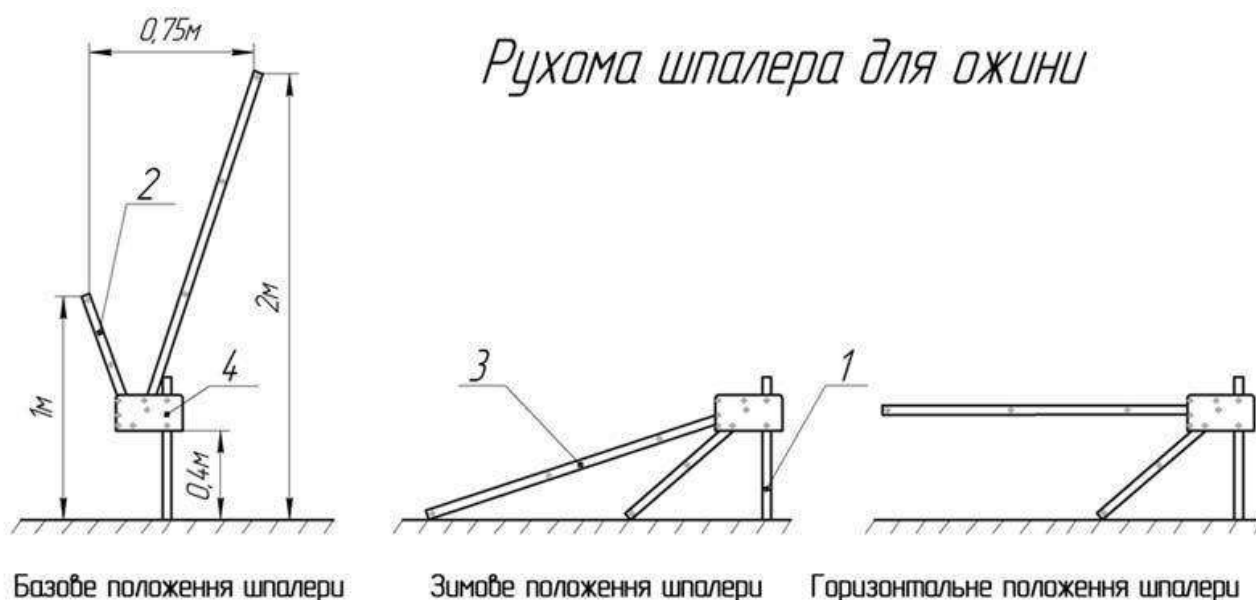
Рухома шпалера для ожини (rotating cross-arm (RCA) technology)
